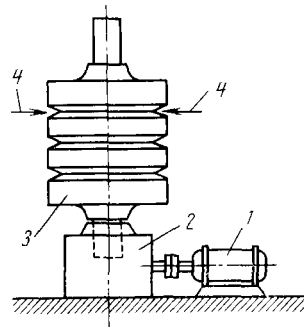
Схема сварки ротора газовой турбины
